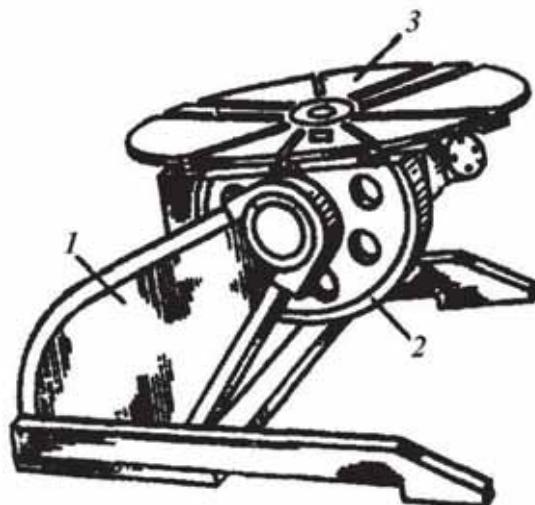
Сварочный манипулятор: 1 – основание; 2 – привод вращения; 3 – стол
